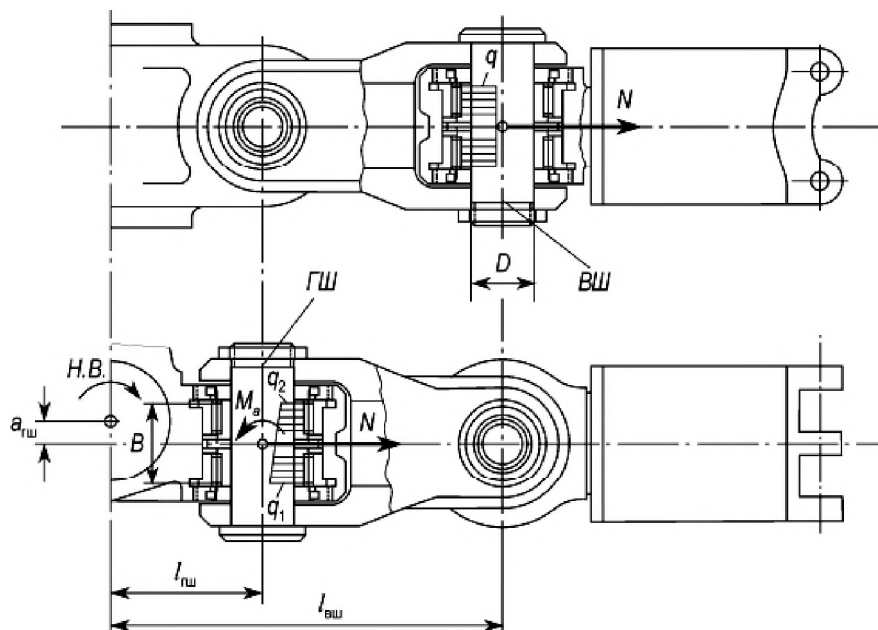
Схема и эпюры нагружения подшипников шарниров втулки НВ:
